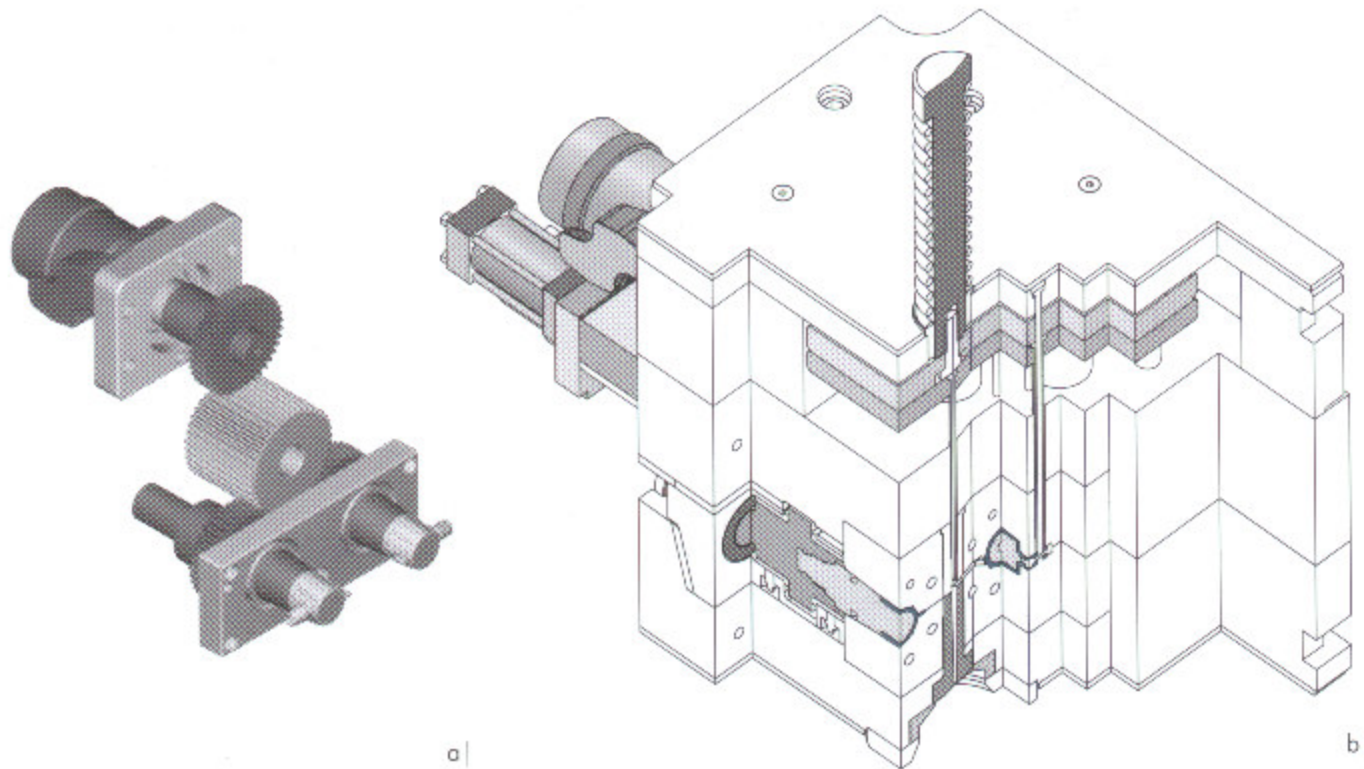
Molde com movimentos rotativos accionados por um motor
